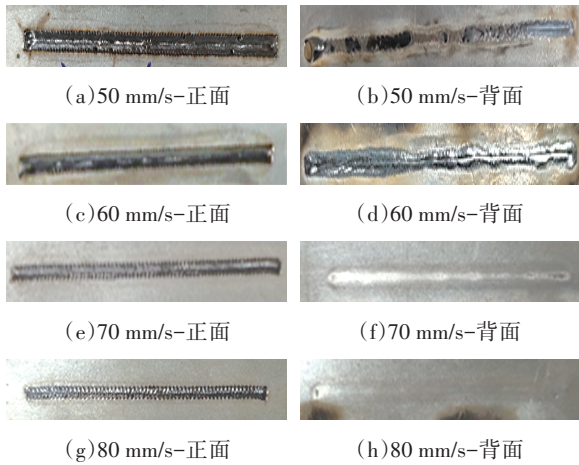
不同焊接速度下上层镀锌钢板表面与背部的焊缝形貌
